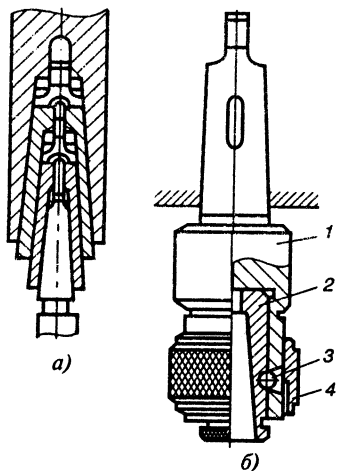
Устройство для закрепления инструмента в сверлильных станках
